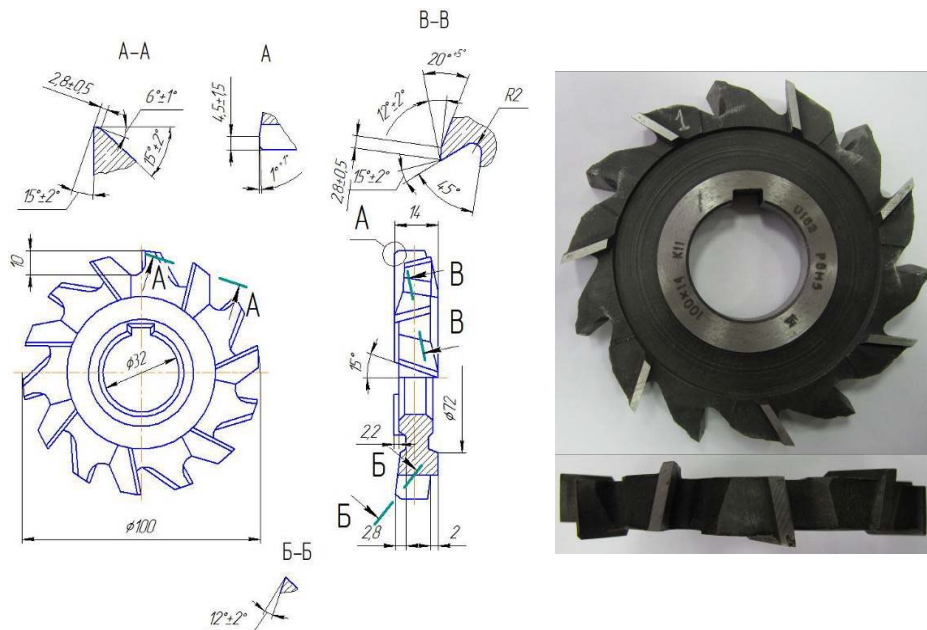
Элементы конструкции и геометрические параметры инструмента
